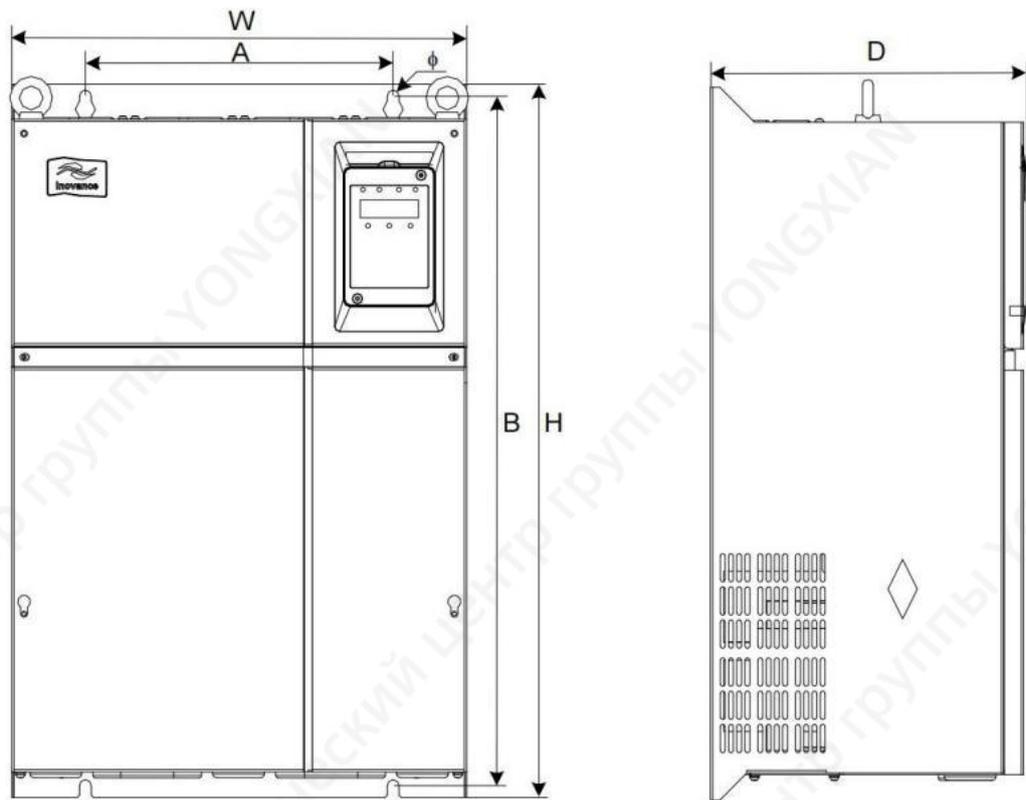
Обзор и установочные размеры листовой металлоконструкции 37-160 кВт
